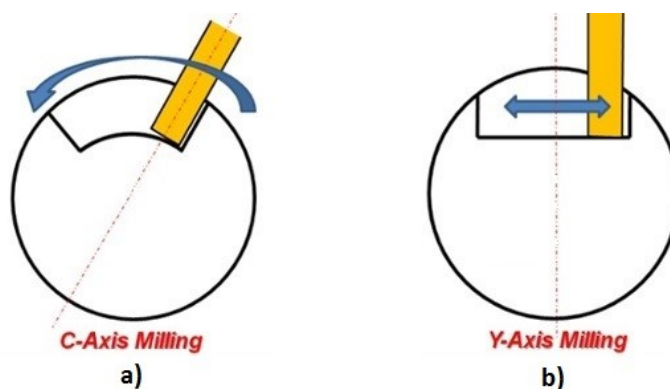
a) Axiální frézování s C osou, b) Radiální frézování s C osou [11]
